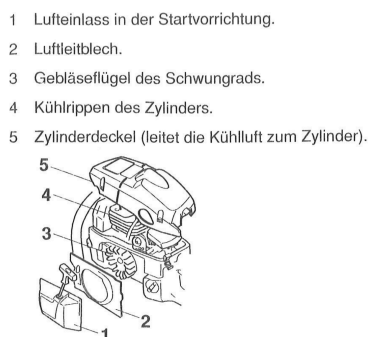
Explosionszeichnung mit Textlegende (Husqvarna 340 2005, S. 35)
